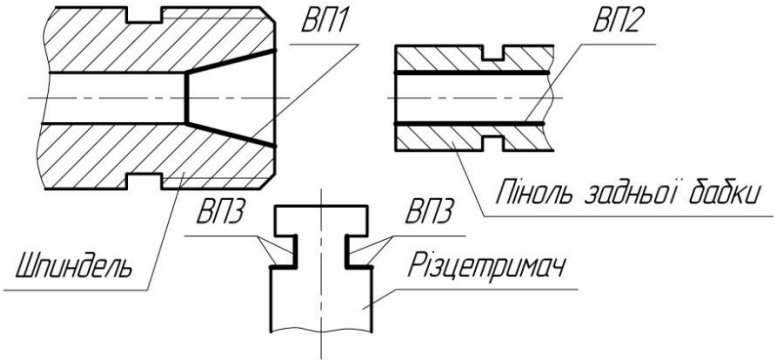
Виконавчі поверхні при обробці вала в центрах
